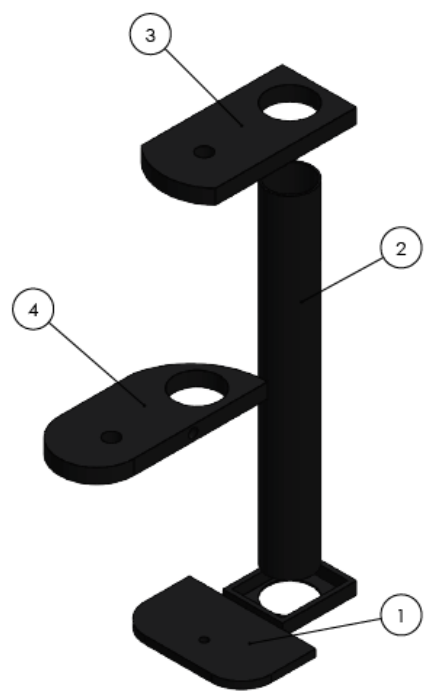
Conjunto Soporte Máquina Equipo Plug Maker.
